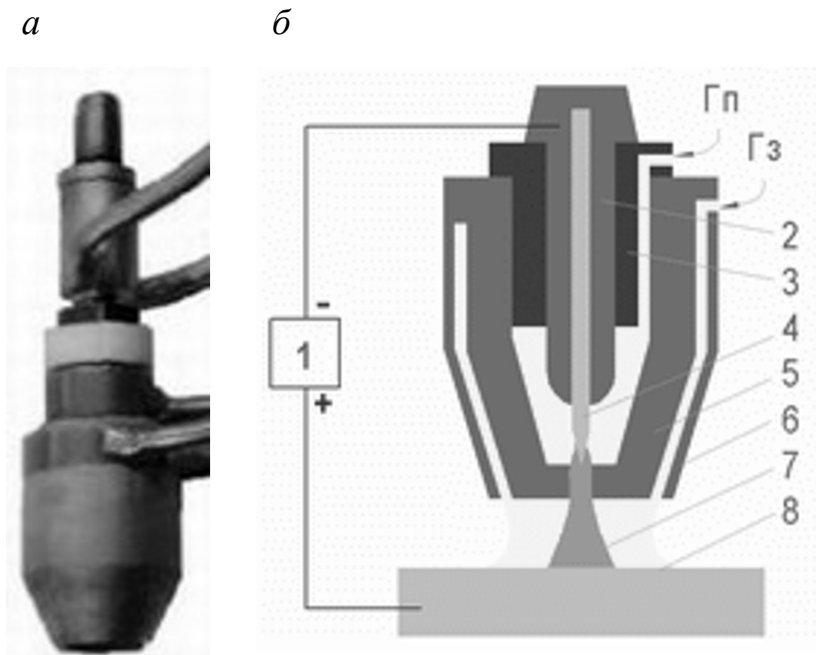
Плазматрон для сварки прямой полярности:
